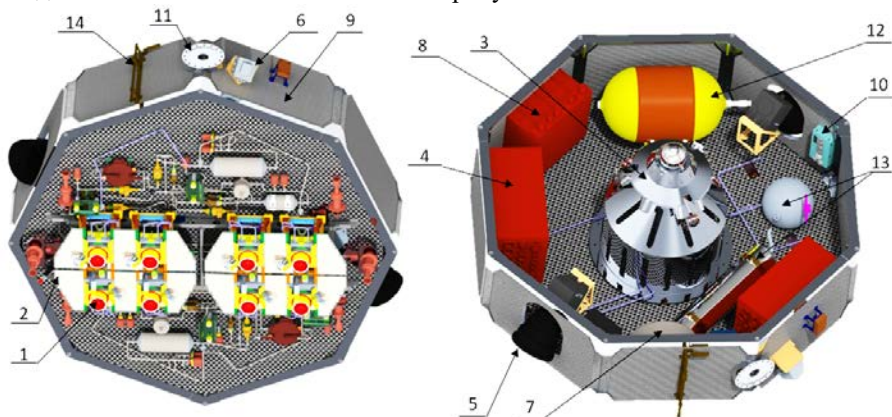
Компоновка приборно-агрегатного отсека МТА:
